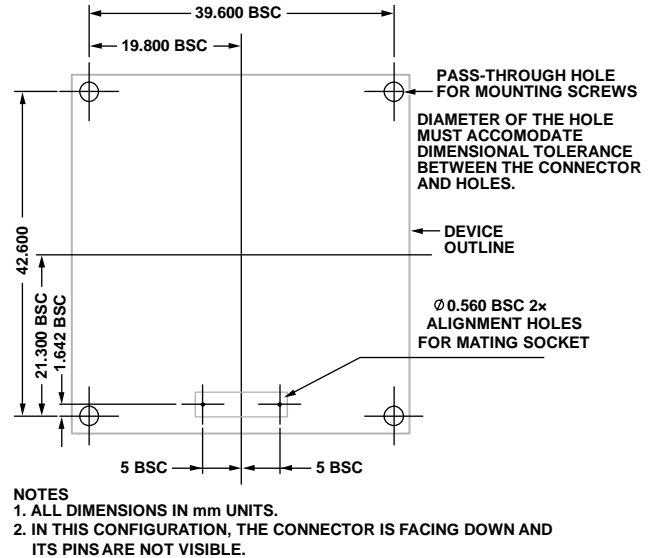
建议PCB焊盘图形布局(连接器朝下)
